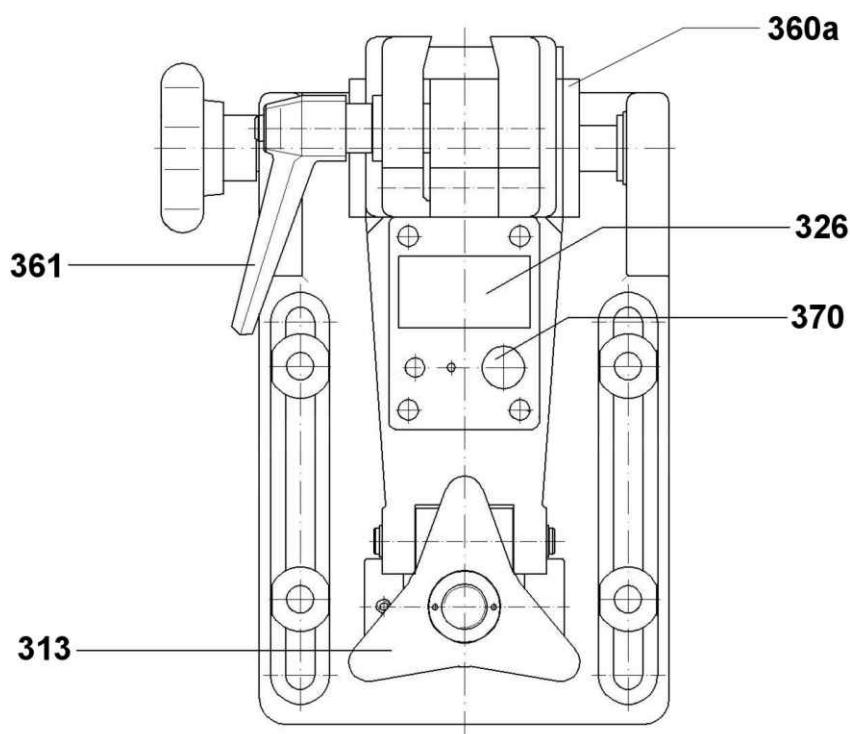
, Установка давлени шлифовани на цифровой каретке
